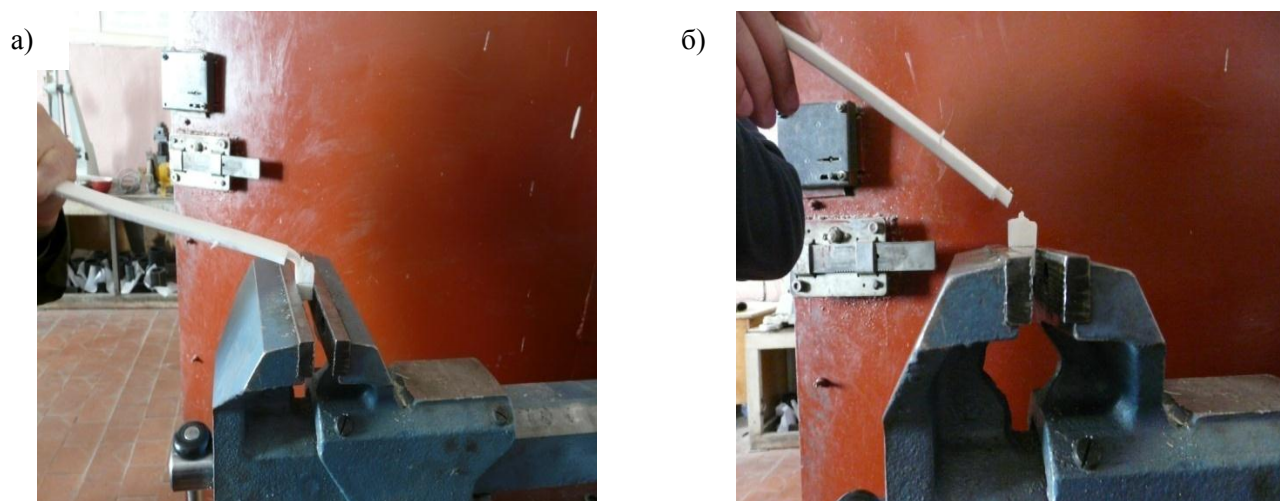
Общий вид испытаний на отдрив образцов сварных соединений:
